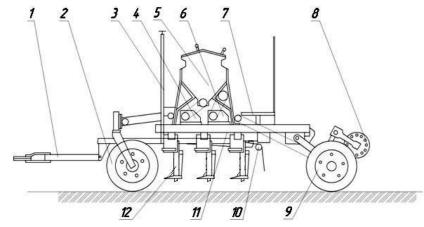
Схема сеялки ССВ-3,5: 1 — дышло; 2 — переднее колесо; 3 — маркёр; 4 — привод зерновых аппаратов; 5 — бункер для семян и удобрений; 6 — привод туковых аппаратов; 7 — площадка; 8 — прикатывающее устройство; 9 — колесо заднее; 10 — выравнивающее устройство; 11 — рама; 12 — сошник
